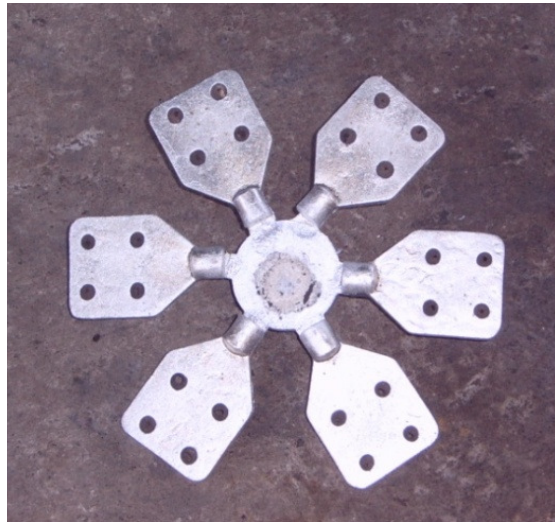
FUNDICIÓN CENTRÍFUGADA
